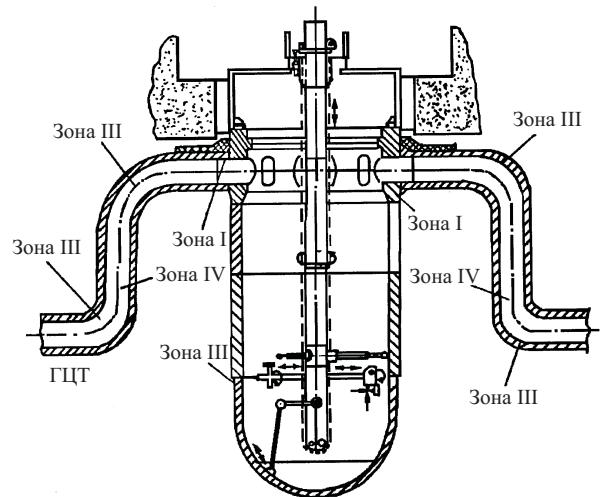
Зоны приварки патрубков ГЦТ к корпусу реактора:
